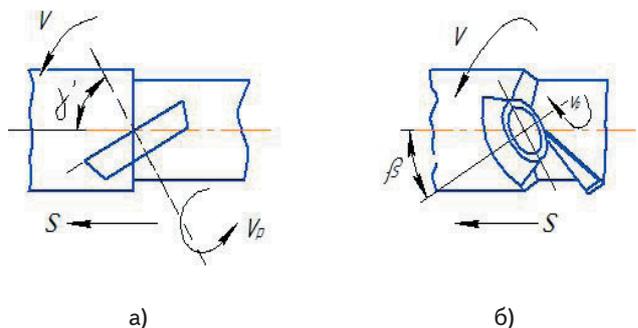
Схема установки чашечного резца: а) первая схема установки; б) вторая схема установки
